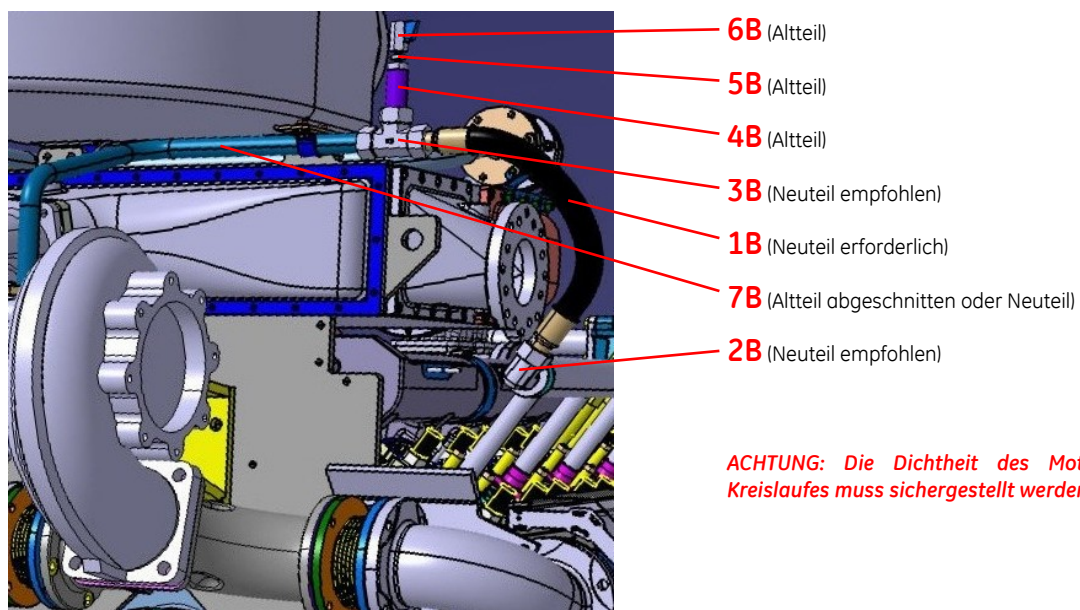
Motorkühlwasser-Rücklaufleitung NACH Installation von Nachrüstpaket B
